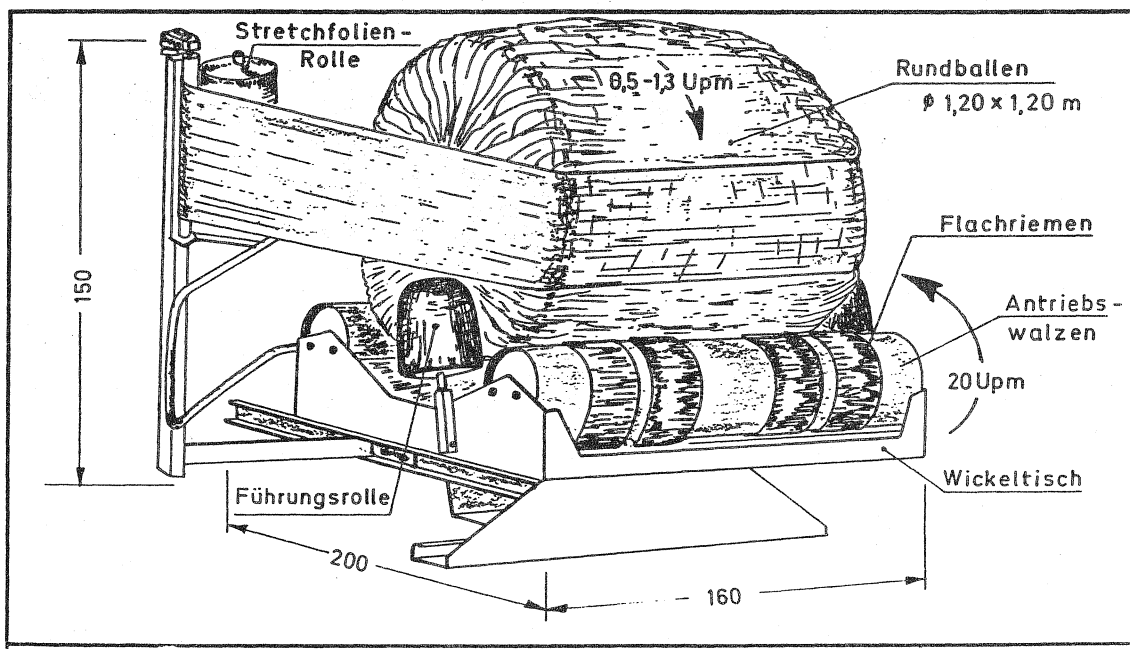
Kverneland-Rundballenwickelmaschine für Heckenbau mit Frontladerbeschickung
